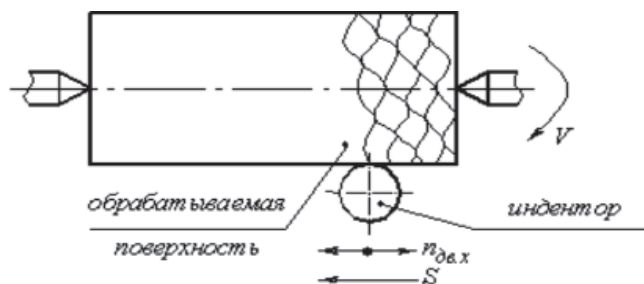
Схема нанесения микрорельефа алмазным выглаживанием
